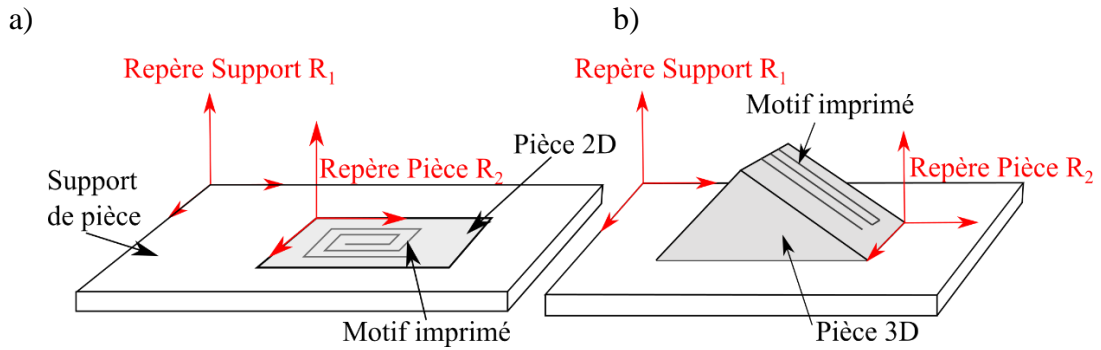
Définition des repères de travail pour repérer des pièces a) 2D b) 3D
